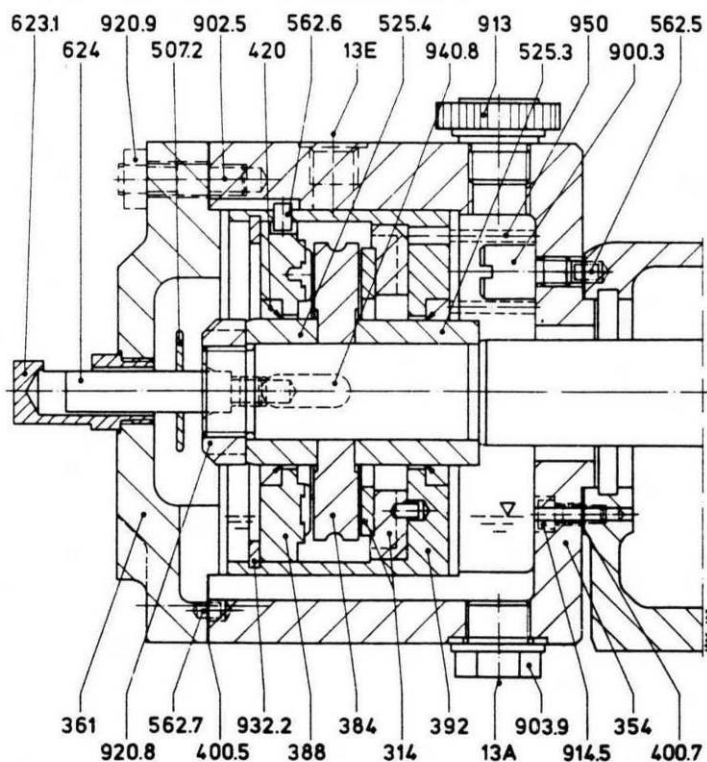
Dispositivo de levantamento: mancal de empuxo segmentado
